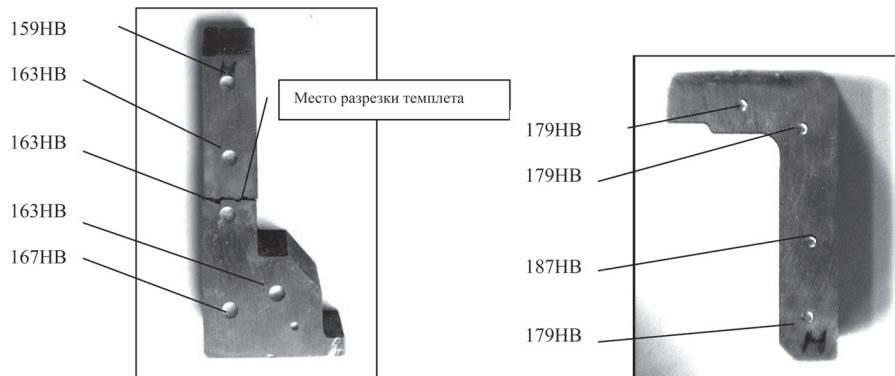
Распределение твердости по сечению образца цельнолитого корпуса водила, изготовленного из высокопрочного чугуна
